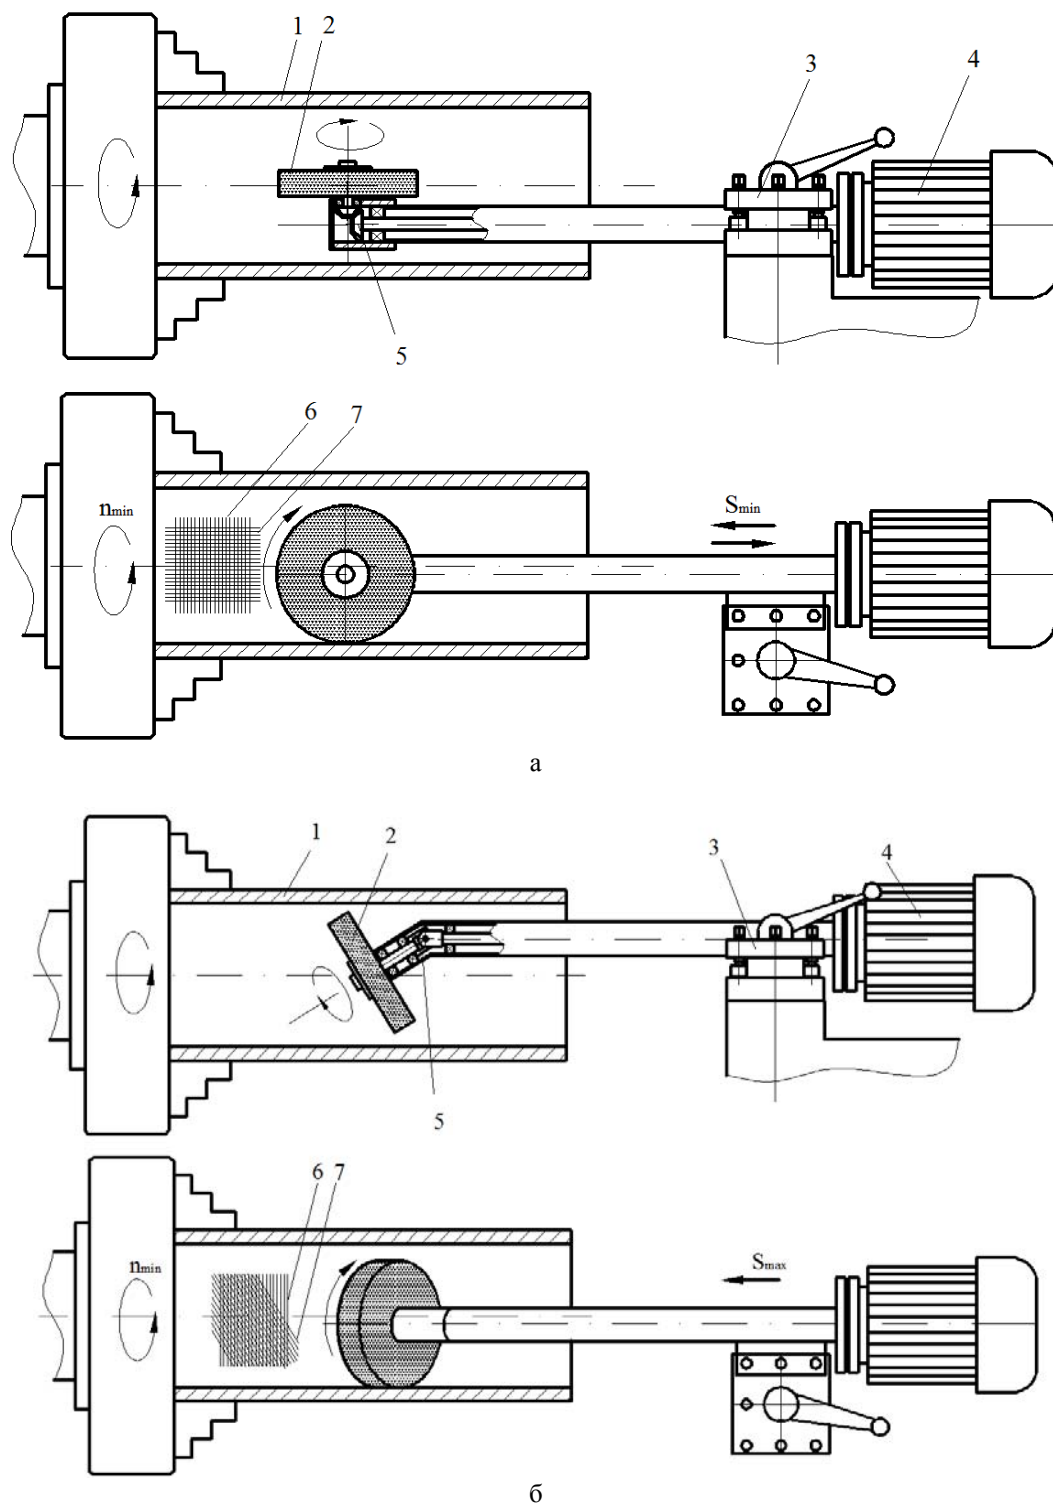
Схемы финишной обработки отверстия цилиндра: 1 – обрабатываемый цилиндр; 2 – войлочный (фетровый) круг; 3 – резцедержатель токарного станка; 4 – электродвигатель; 5 – коническая зубчатая передача (а) и шарнир Гукса (б); 6 – обработочные риски после растачивания; 7 – обработочные риски после шлифования ( $S_{min}$ ,  $S_{max}$  – значения подачи;  $n_{min}$  – частота вращения шпинделя)
